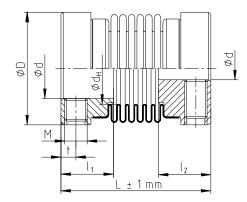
TOOLFLEX® Bauart M mit Gewindestift (Ausf. 1.1)
